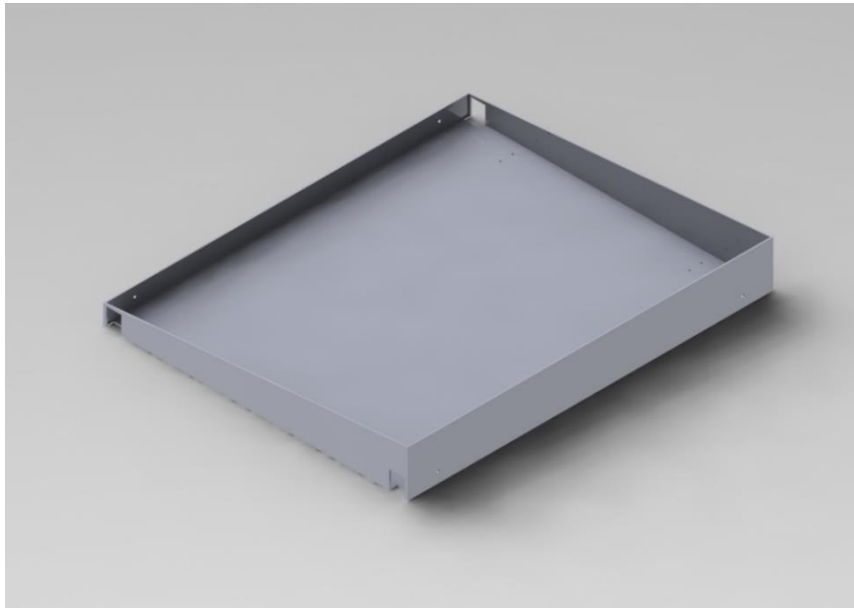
Ensamblaje subconjunto 1.4. Soldadura 6, 7 y 8.
